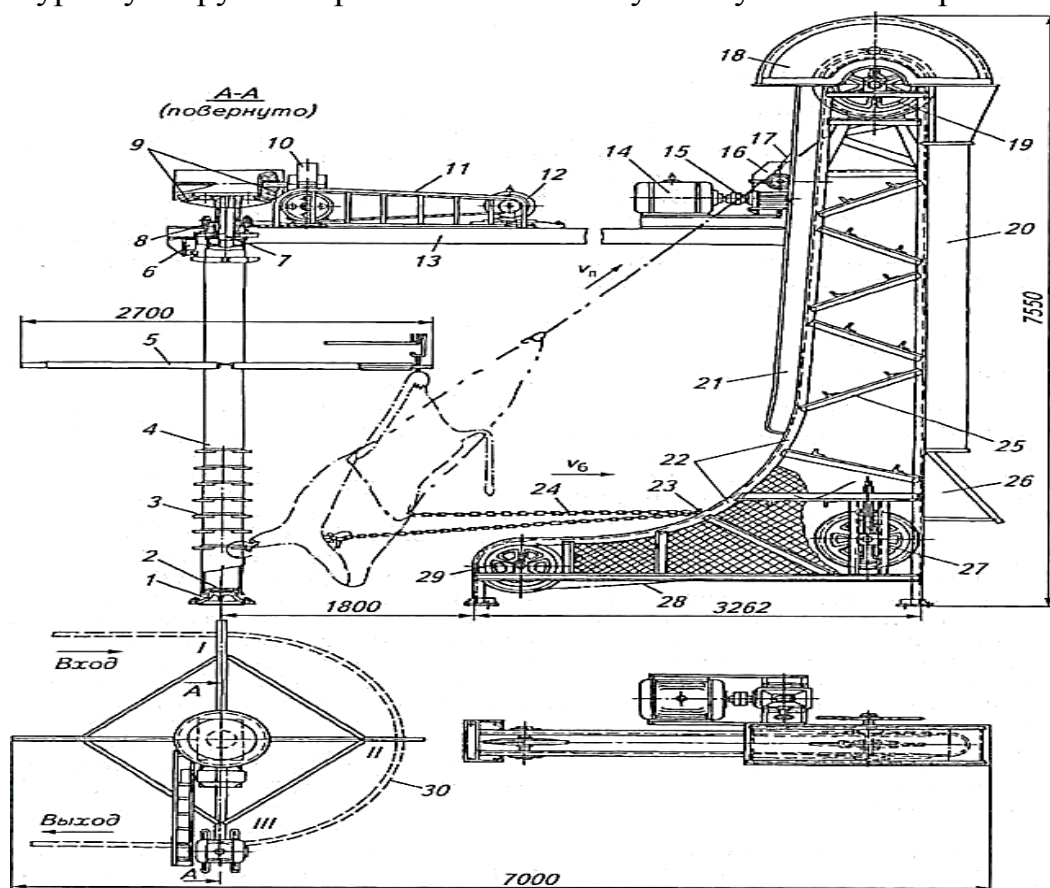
Установка ФУАМ для съемки шкур с туш крупного рогатого скота: 1 – опора; 2 – упорный подшипник; 3 – скобы; 4 – стойка; 5 – рычаг; 6 – конечный выключатель; 7 – хвостовик; 8 – подшипник; 9 – коническая зубчатая передача; 10, 16 – червячные редукторы; 11 – клиноременная передача; 12, 14 – электродвигатели; 13 – каркас; 15 – муфта; 17 – цепная передача; 18 – кожух; 19 – приводная звездочка; 20 – желоб; 21 – лоток; 22 – направляющая; 23 – крюк; 24 – цепь крепления шкуры; 25 – рама; 26 – склиз; 27 – натяжная звездочка; 28 – тяговая цепь; 29 – оборотная звездочка; 30 – рельс; v_6 – допустимая предельная скорость съемки шкуры в боковом направлении (0,1 м/с); v_n – допустимая предельная скорость съемки шкуры в продольном направлении (0,13...0,17 м/с)
